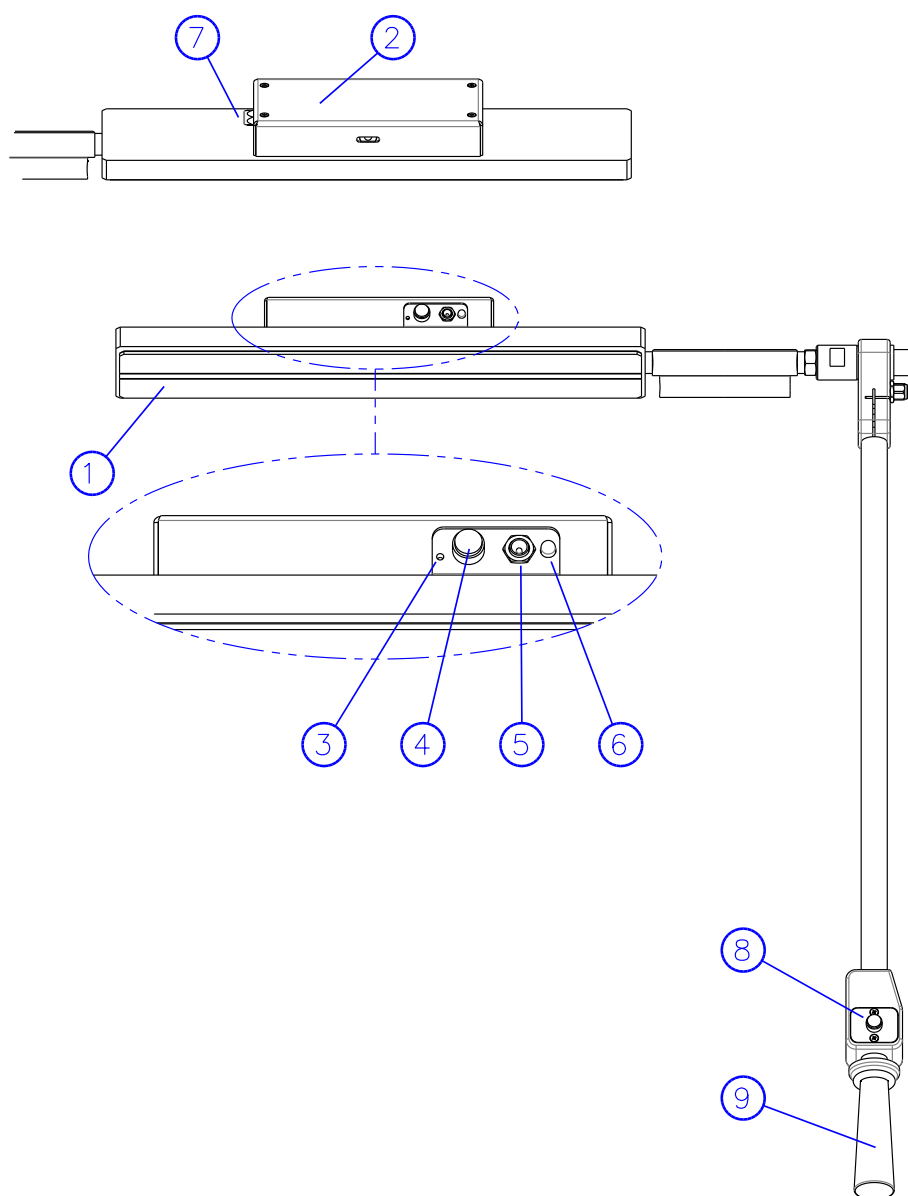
Ausrichtungslaser und Spiegelmontage
